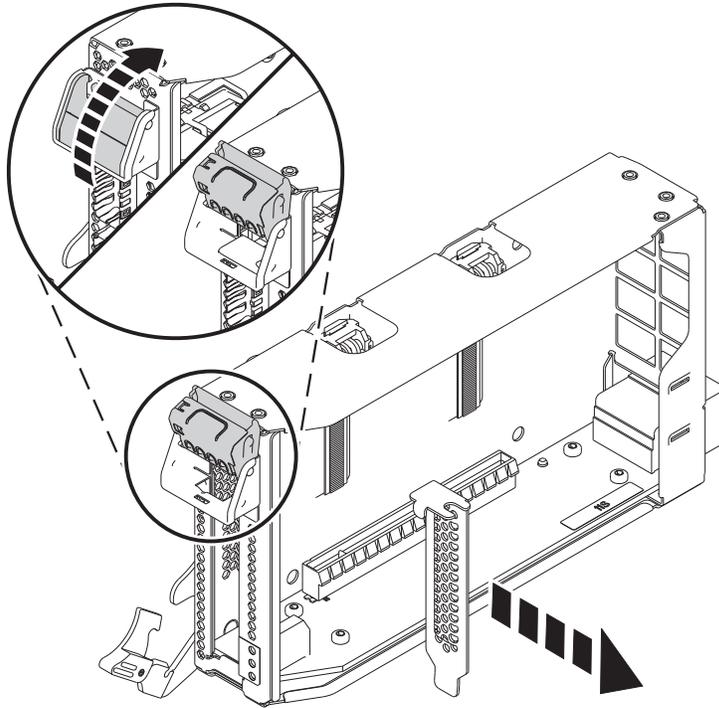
Remover o preenchimento do adaptador PCIe da cassetete do adaptador
